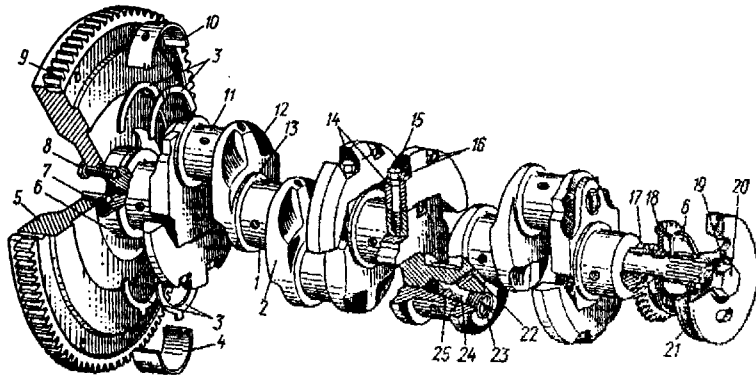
Коленчатый вал с маховиком (Д-240): 1 – коренная шейка; 2 и 12 – щеки; 3 – упорные кольца; 4 – нижний вкладыш коренного подшипника; 5 – маховик; 6 – маслоотражательная шайба; 7 – установочный штифт; 8 – болт; 9 – зубчатый венец; 10 – верхний вкладыш коренного подшипника; 11 – шатунная шейка; 13 – галтель; 14 – противовесы; 15 – болт крепления противовеса; 16 – замковая шайба; 17 – шестерня коленчатого вала; 18 – шестерня привода масляного насоса; 19 – упорная шайба; 20 – болт; 21 – шкив; 22 – канал подвода масла в полость шатунной шейки; 23 – пробка; 24 – полость в шатунной шейке; 25 – трубка для масла
